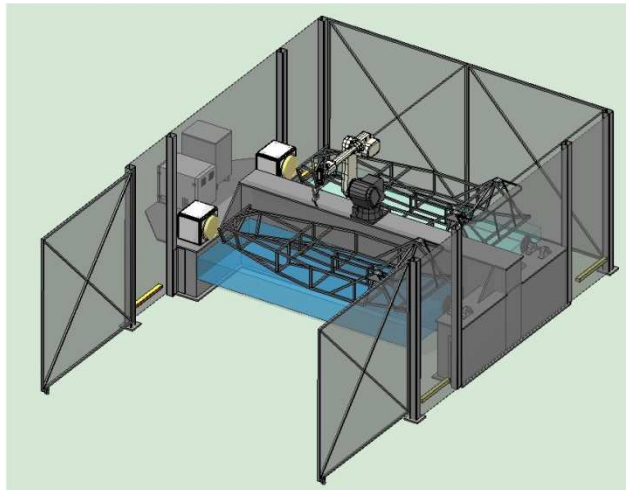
IMAGEM ILUSTRATIVA DE UMA CÉLULA DE SOLDADURA ROBOTIZADA
